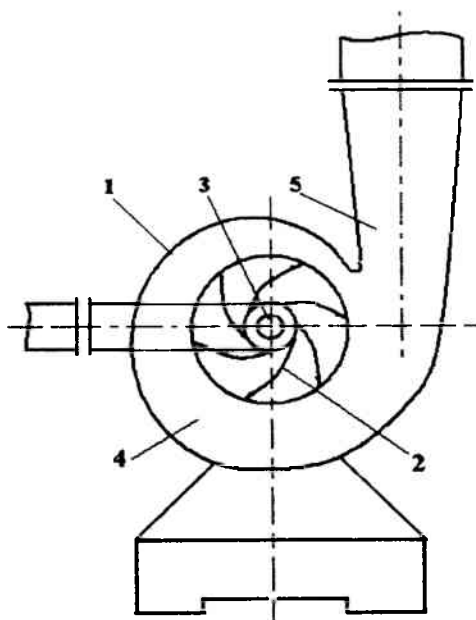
Схема лопастной машины центробежного типа [2]:
